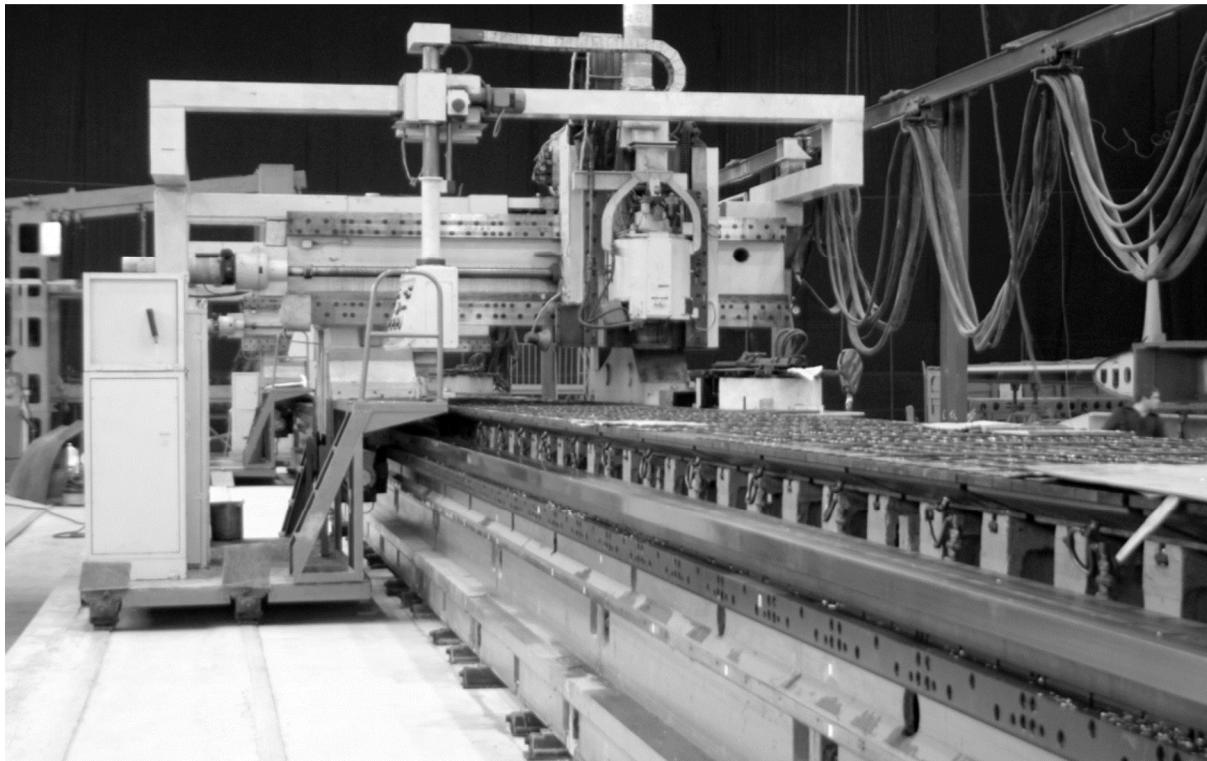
Фрезерний верстат із ЧПК для виготовлення довгомірних деталей крила
